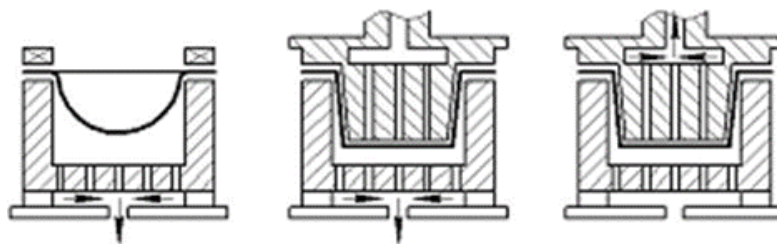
Схема позитивного формування з попередньою витяжкою вакуумом
